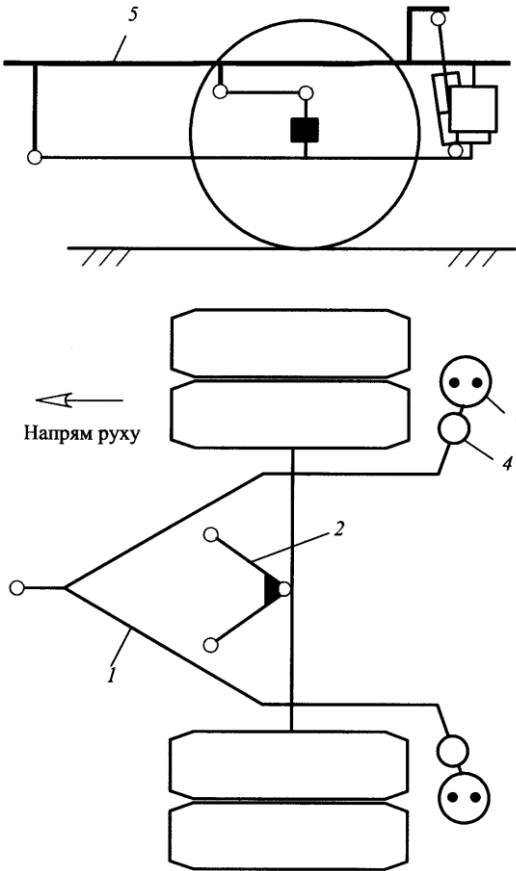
Схема передньої пневматичної підвіски:
